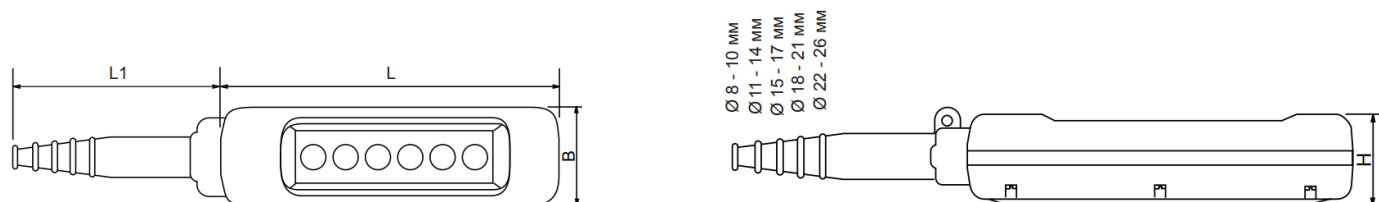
Габаритные и установочные размеры поста кнопочного
